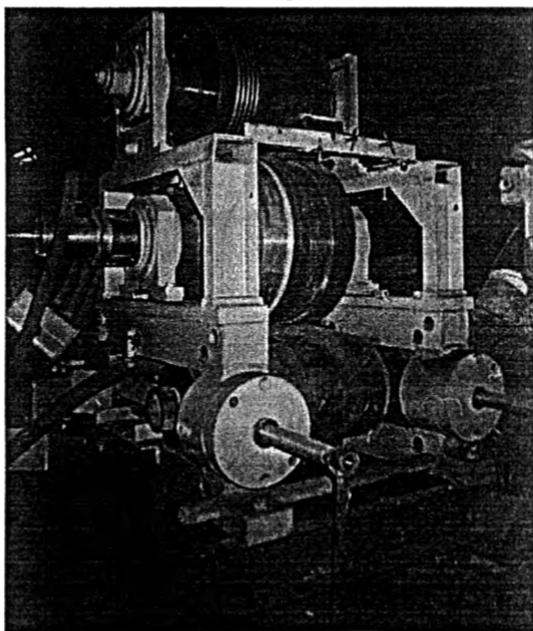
Экспериментальная установка непрерывного литья в кристаллизатор типа колесо – лента
